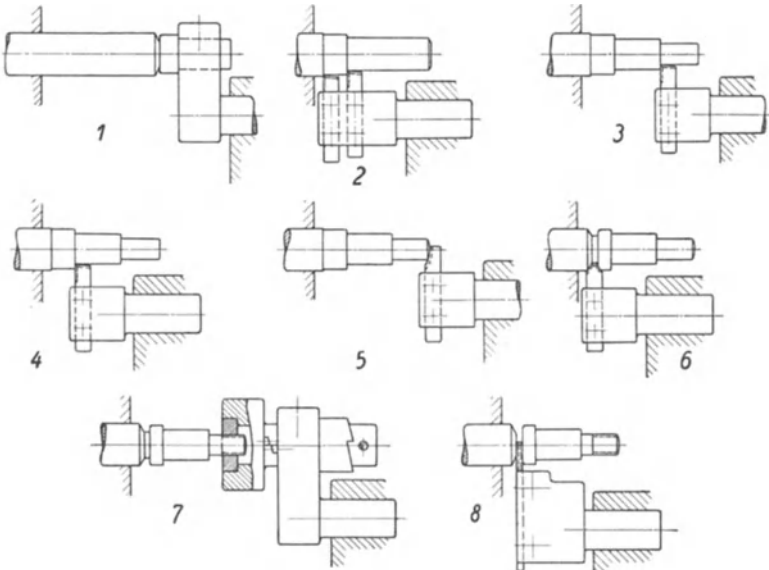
Arbeitsplan für wagrecht gelagerten Revolverkopf — Stangearbeit. Bolzen. Diese Abbildung zeigt denselben Bolzen, der auf Abb.'47 auf einem senkrecht gelagerten Kopf bearbeitet wurde. — 1. Anschlag. — 2. 1. Ansatz und Bund drehen. — 3. Gewindepapfen drehen. — 4. Ansatz schlichten. — 5. Abrunden. — 6. Einstechen. — 7. Gewindeschneiden. — 8. Abstechen.
